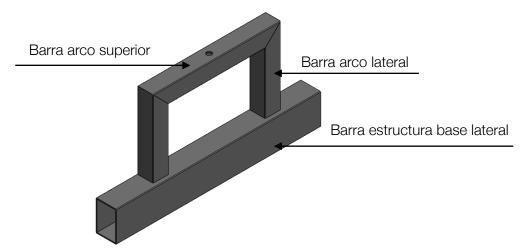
Vista isométrica de las barras soldadas. Fuente: elaboración propia.
